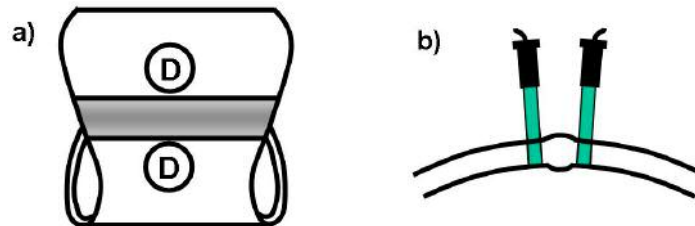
Dopplungsprüfung in der Wärme-Einflusszone. a) Draufsicht auf das Prüfkopfpaar bezüglich der Schweißnaht; b) Querschnitts-Ansicht von Prüfkopfpaar und Schweißnaht.
